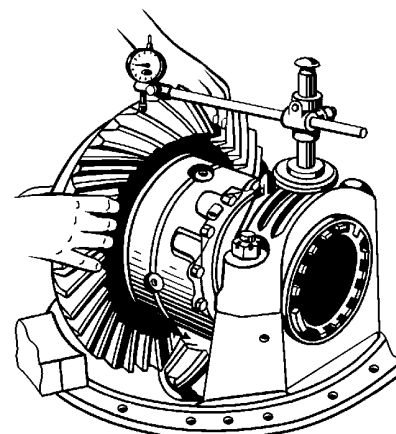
Измерение бокового зазора в зацеплении шестерен главной передачи
